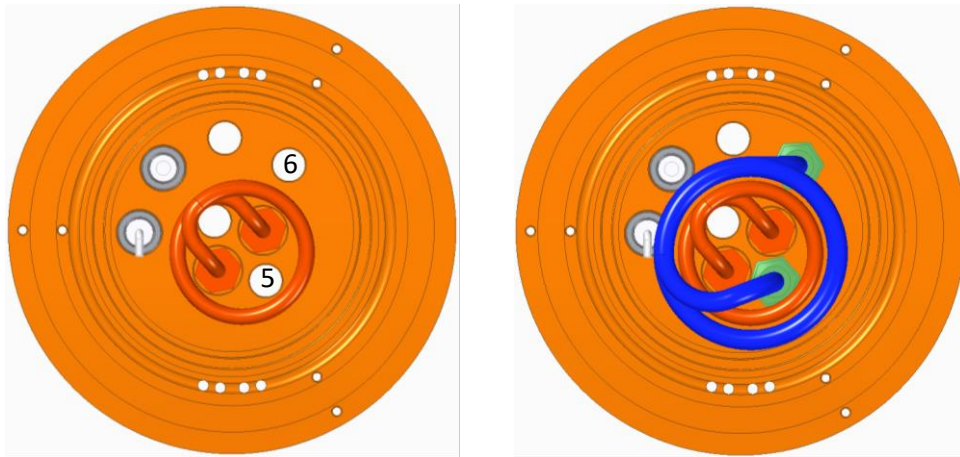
Draufsicht des Boilerbodens zur Montage der Wasserwendel in den Bohrungen 5 und 6
